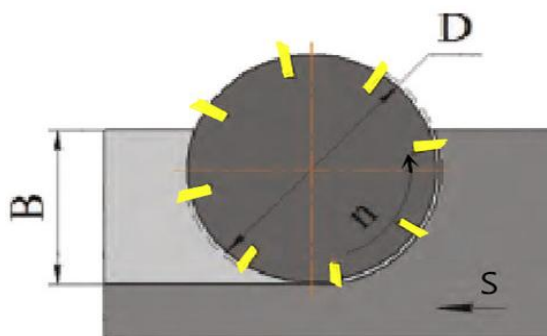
Встречное фрезерование при левом вращении фрезы
